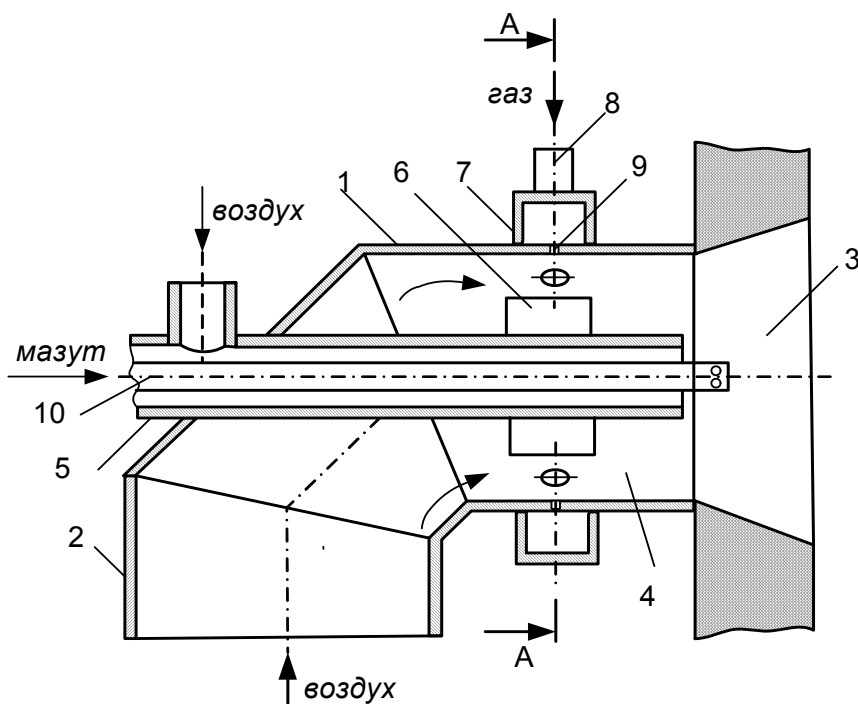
Газомазутная горелка новой конструкции: 1-корпус; 2-патрубок для подачи воздуха; 3-амбразура; 4-смесительная камера; 5-труба для подачи воздуха; 6-вставка; 7-кольцевой коллектор; 8-патрубок для подачи газа; 9-газораздающие отверстия; 10-мазутная форсунка
